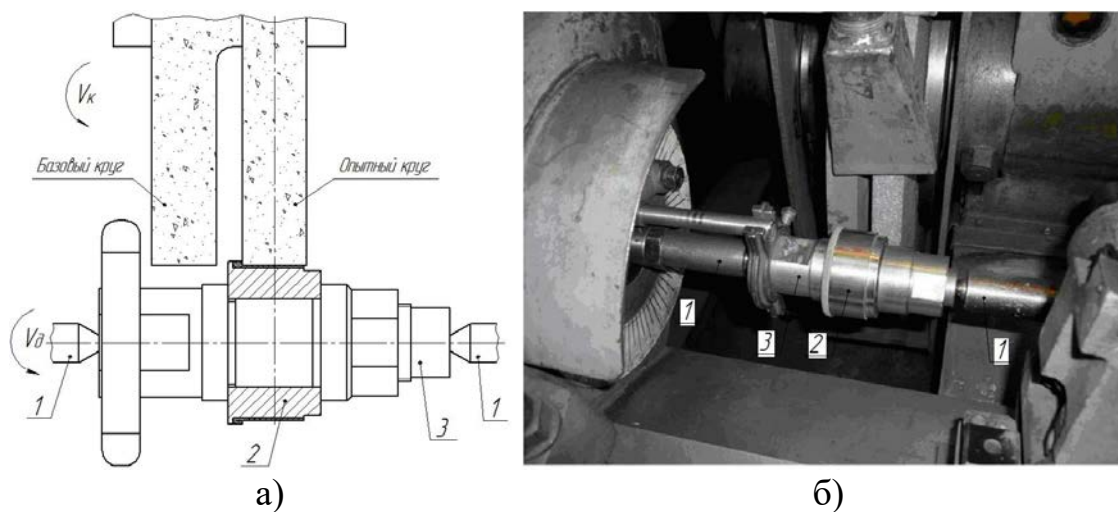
Экспериментальная установка для проведения исследований по шлифованию: а – принципиальная схема; б – общий вид рабочей зоны станка
